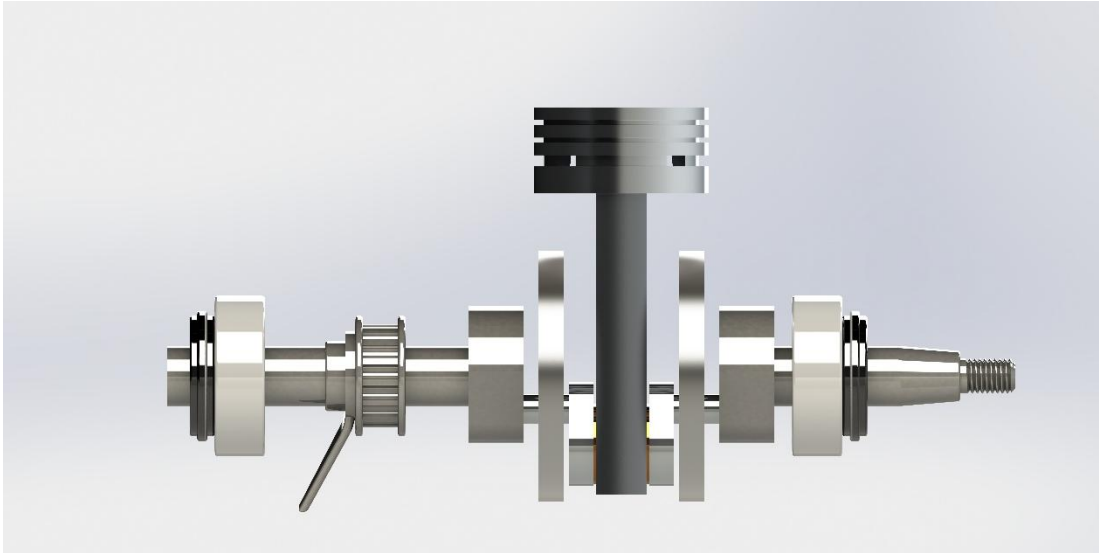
Vista frontal da montagem do protótipo do motor hipocicloide.
